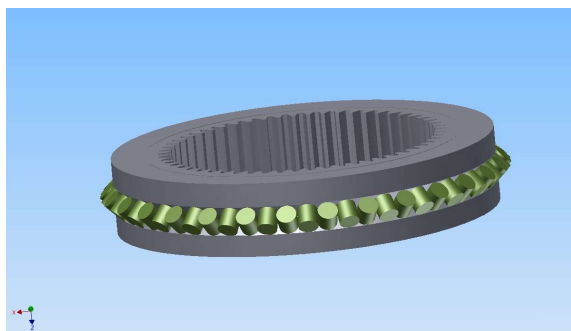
Бессепараторный роликовый опорно-радиальный подшипник, с совместно выполненным крупномодульным зубчатым колесом порталного крана мод. КБ-572Б [12]
